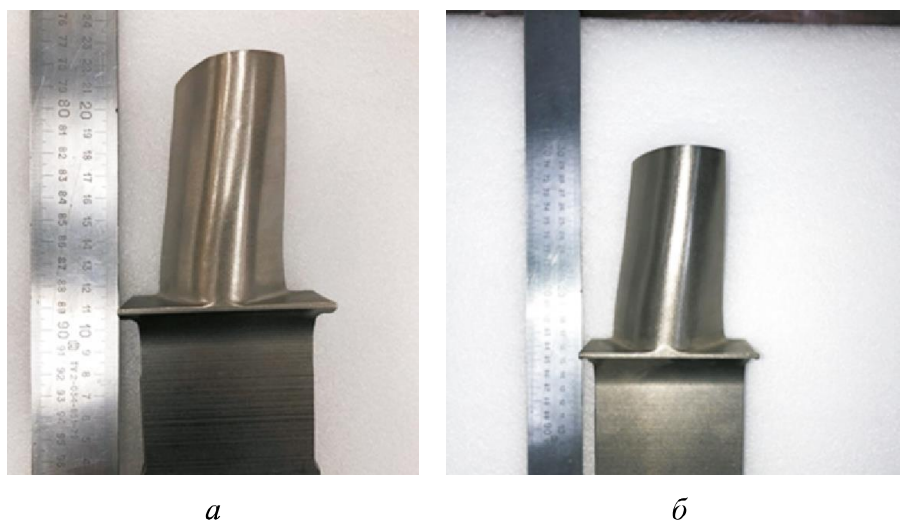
Внешний вид рабочих лопаток турбины приводов газоперекачивающих агрегатов ГТК-10И (а) и ГТК-25И (б)
